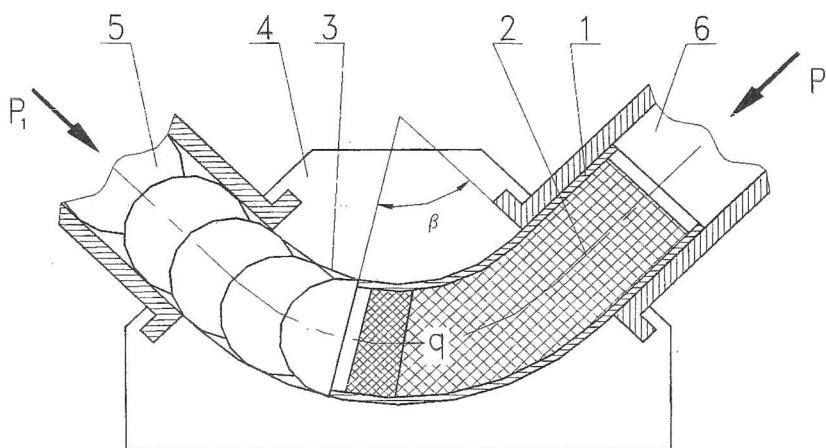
Способ изготовления гибкой крутоизогнутых патрубков
